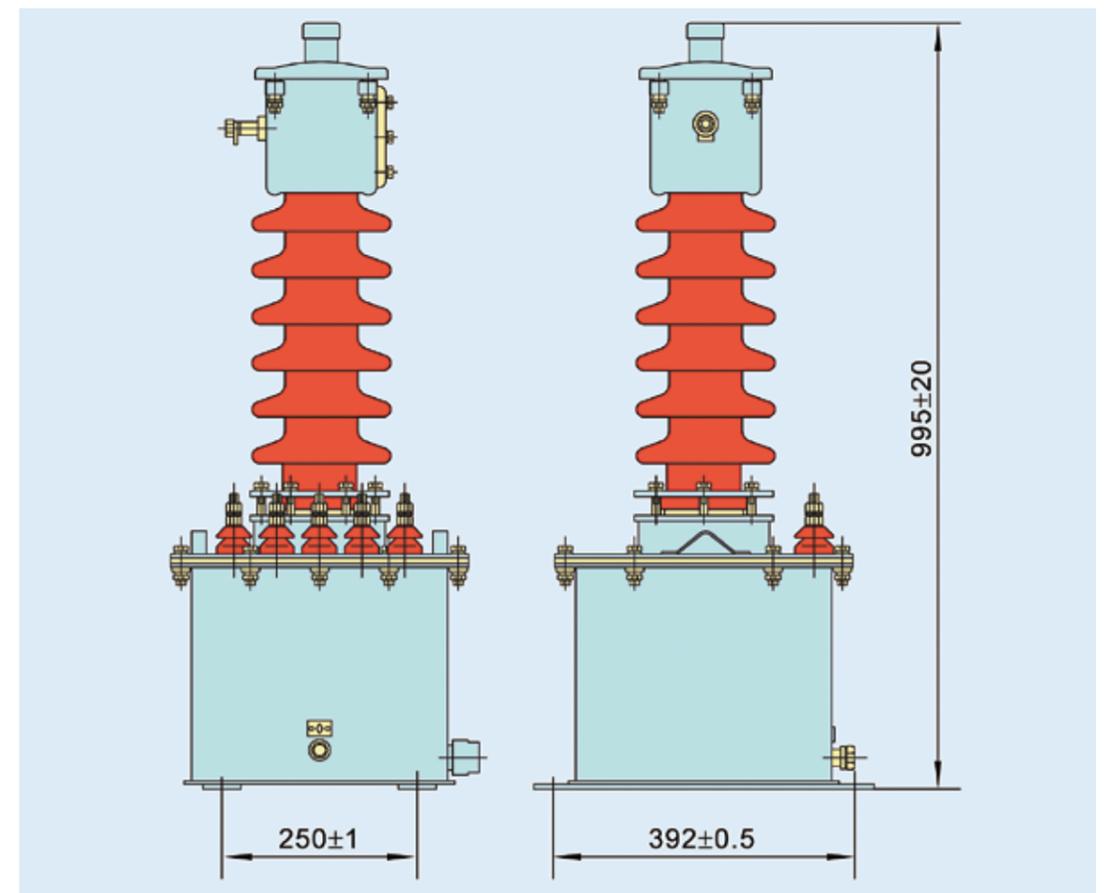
Внешний вид и размеры трансформатора напряжения JDXN2-35W2
